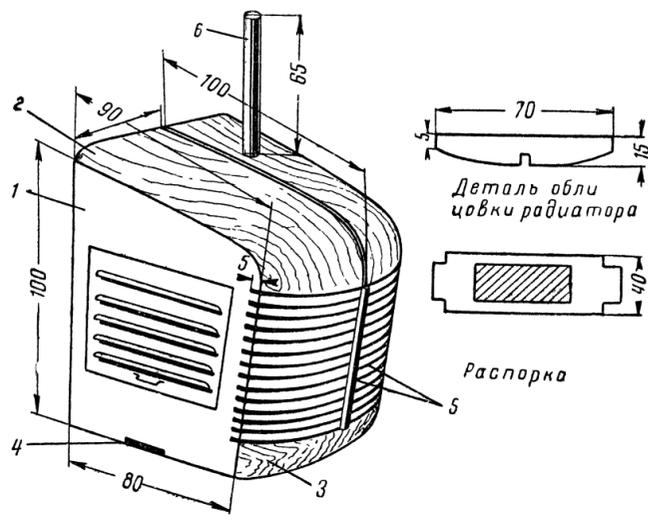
Капот: 1—боковинка капота; 2—верхний брусок; 3—нижний брусок; 4—распорка; 5—детали облицовки радиатора; 6—выхлопная труба
